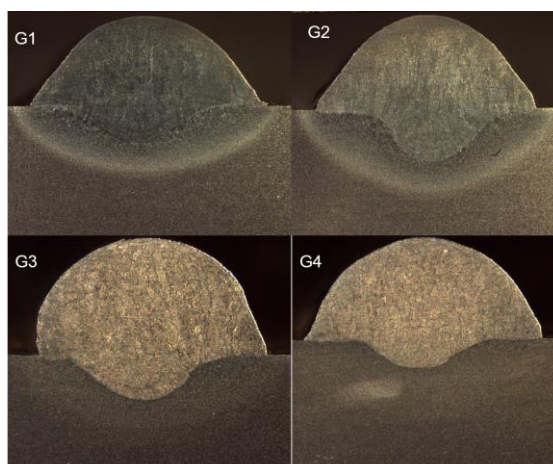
Seção transversal do cordão de solda referente à cada condição de soldagem
